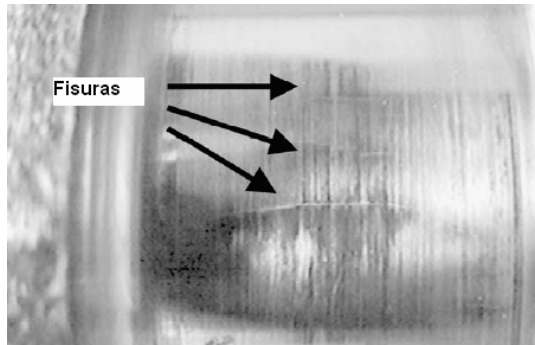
Detalle del muñón del cigüeñal con fisuras [2]
